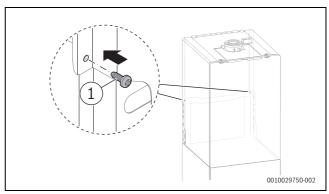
Visser fermement les panneaux latéraux de l'habillage sur les côtés gauche et droit
